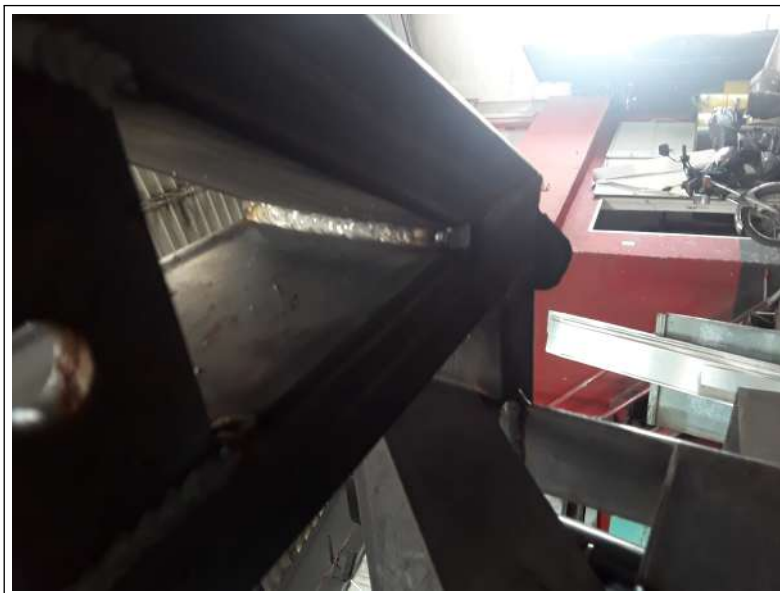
Falta de penetración de soldadura.
